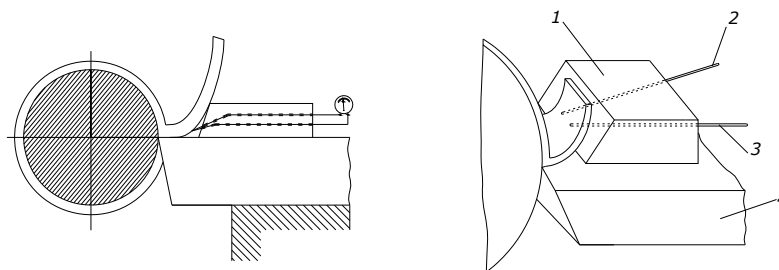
Вимірювання температури стружки за допомогою ковзаючої термопару: 1- твердосплавна підставка; 2-платина; 3 - платинородій; 4 -різець
